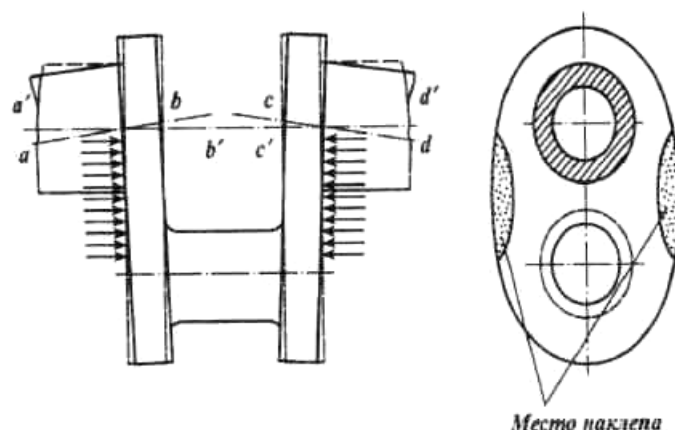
Схема правки наклепом шеек коленчатого вала:
